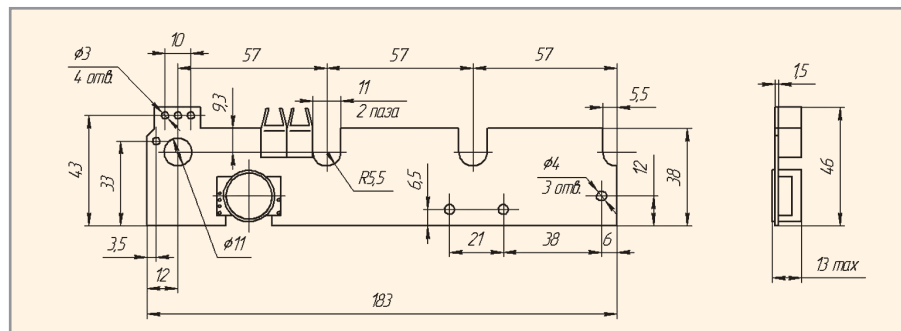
Габаритные и установочные размеры модуля 1МУБ180
